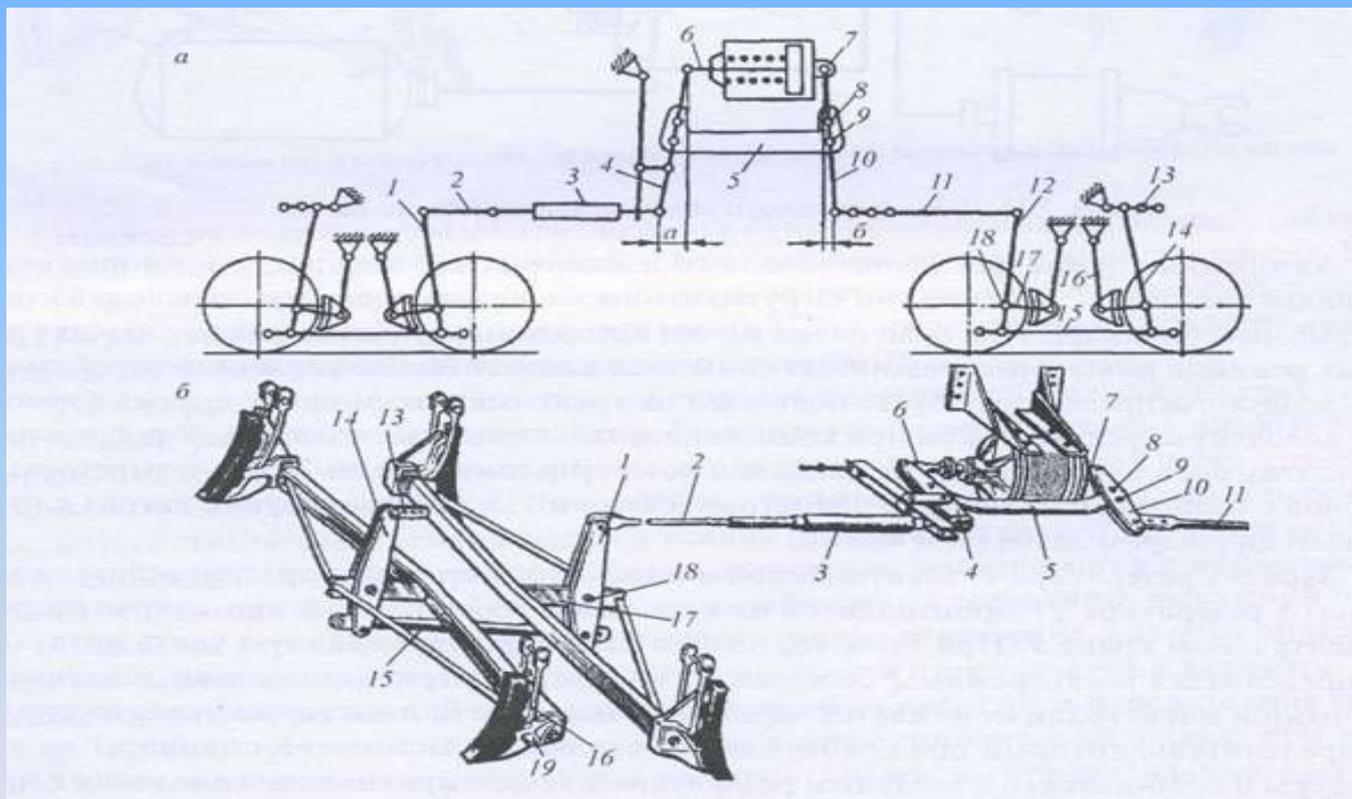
Схема (а) и конструкция (б) рычажной передачи четырехосного грузового вагона
